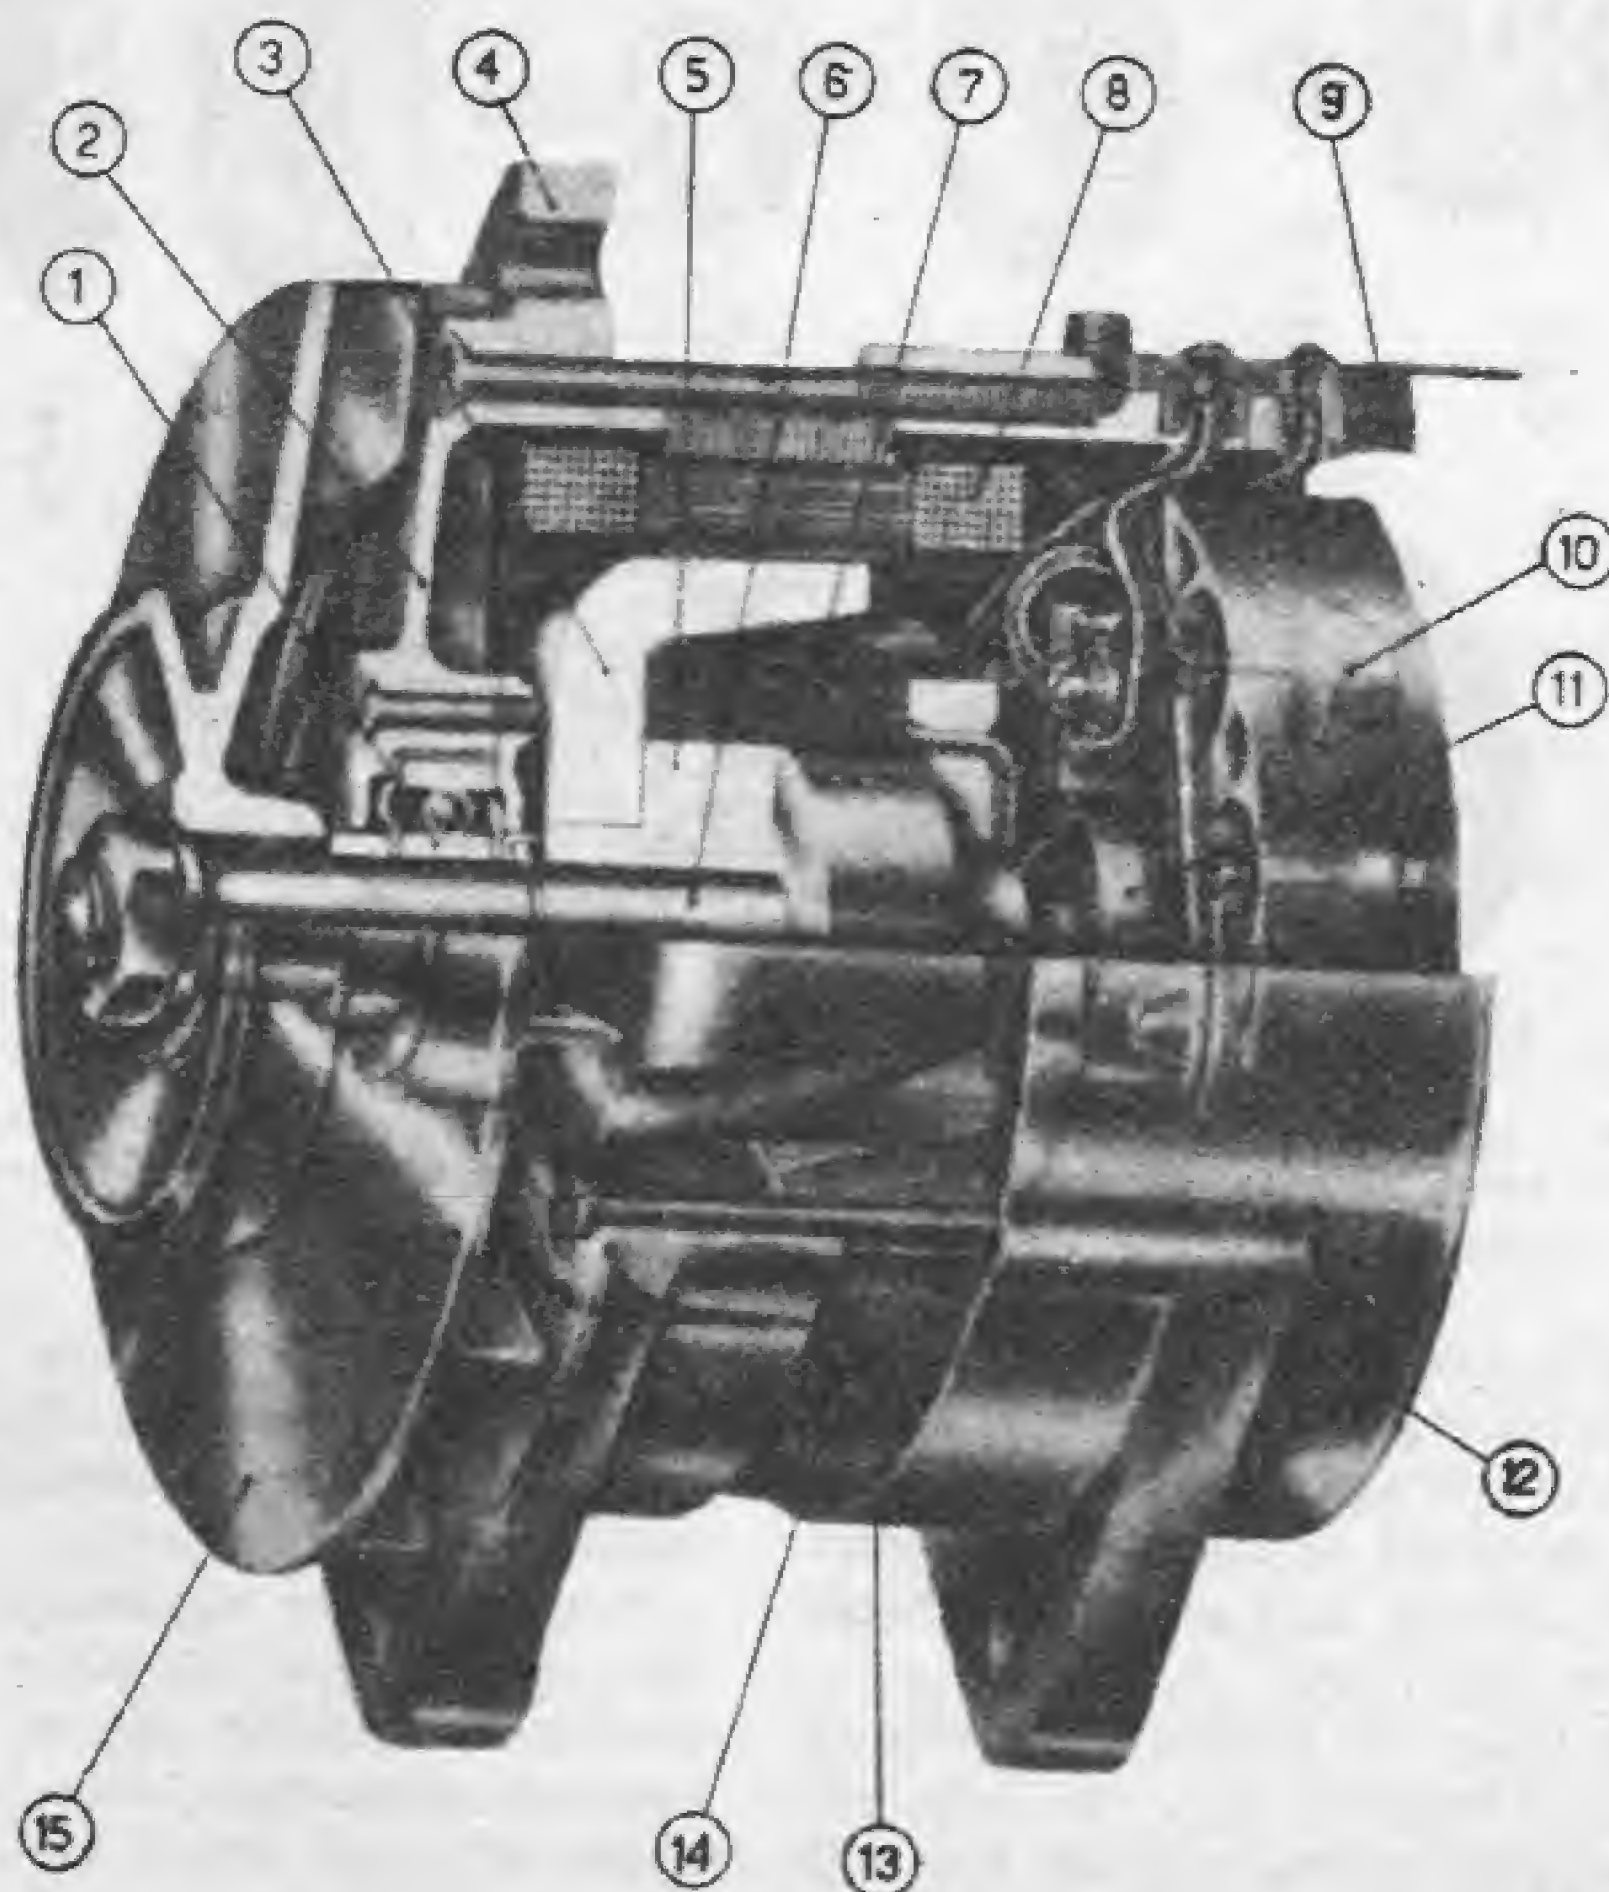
Alternador Marelli; 1) cojinete a bolillas; 2) soporte del lado de mando; 3) y 5) rotor; 4) oreja de fijación; 6) eje del rotor; 7) bobina de excitación; 8) bobinado del estator; 9) soporte de los bornes de las escobillas; 10) diodos; 11) anillo colector; 12) soporte del lado diodos; 13) núcleo del estator; 14) tirante; 15) polea.
